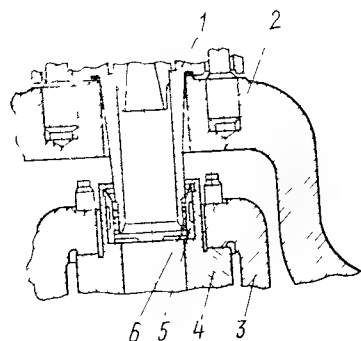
Крепление паровпуска в двухстенный корпус турбины
